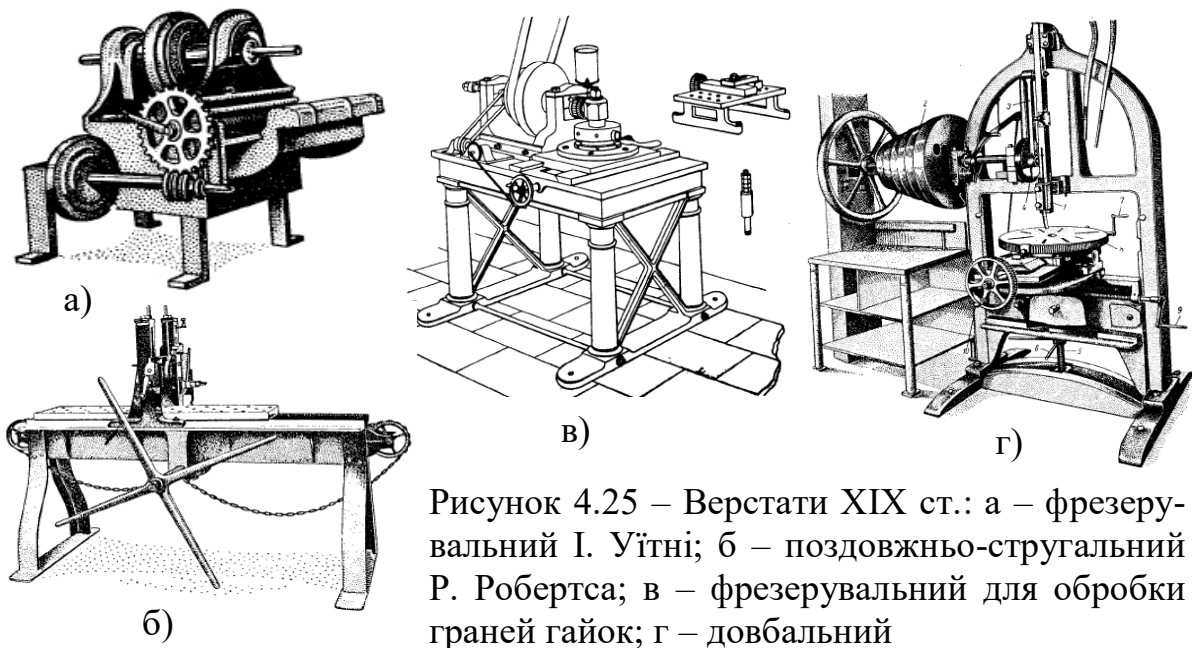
Верстати XIX ст.: а – фрезерувальний І. Уїтні; б – поздовжньо-стругальний Р. Робертса; в – фрезерувальний для обробки граней гайок; г – довбальний
